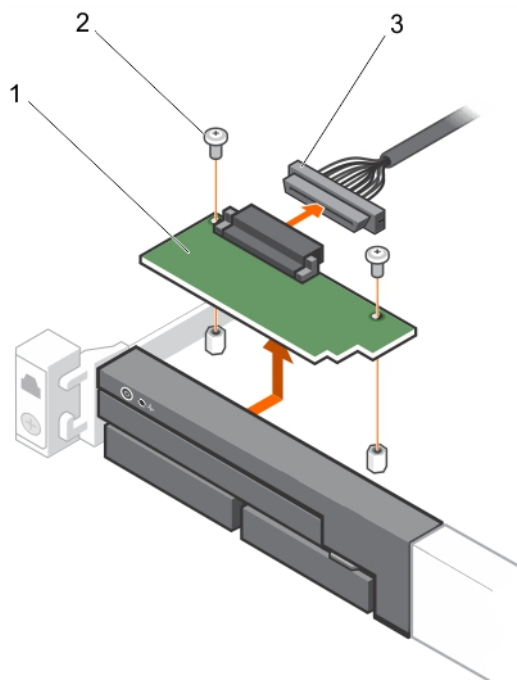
Entfernen des Bedienfeldmoduls – Gehäuse mit acht Festplatten
